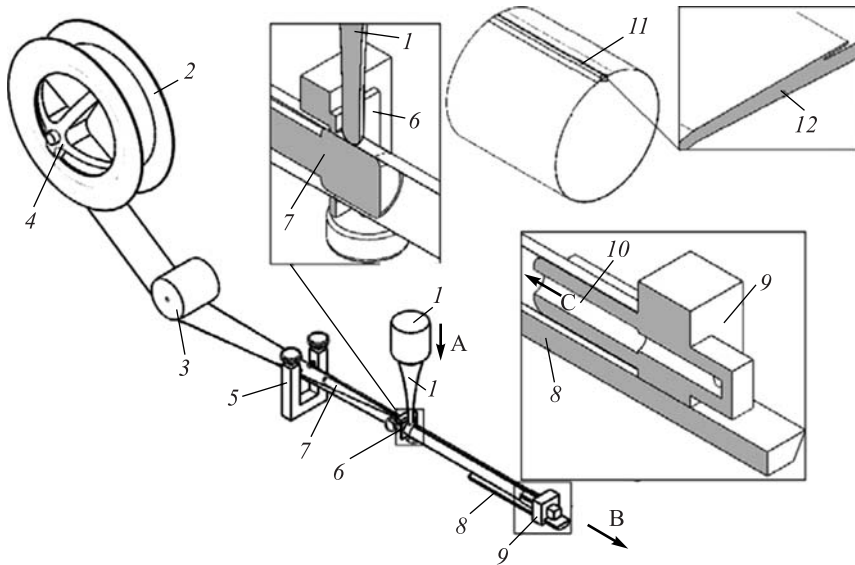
Блок-схема устройства для сварки строу-трубок: 1 — сопло; 2 — бобина с пластиковой лентой; 3, 4 — два регулируемых устройства натяжения ленты; 5 — U-образный профиль; 6 — фильера; 7 — цилиндрическая наковальня; 8 — направляющая для перемещения каретки 9 с соплом 10; 11, 12 — сварной шов. А — положение соплода, фильеры и наковальни при сварке строу; В — направляющая для каретки с соплом подачи воздуха; С — направление подачи воздуха
